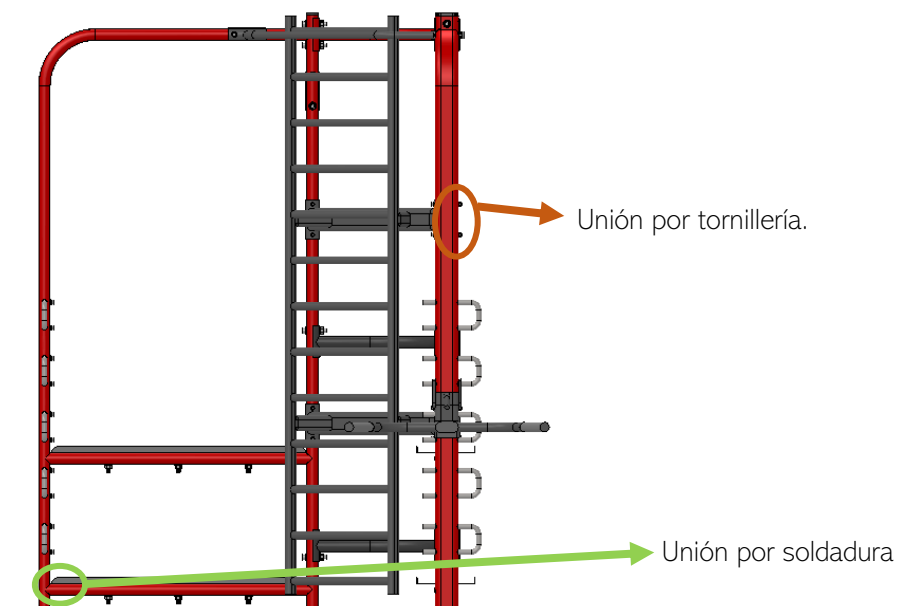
Soldadura y uniones del subconjunto 2. Fuente: Elaboración propia
